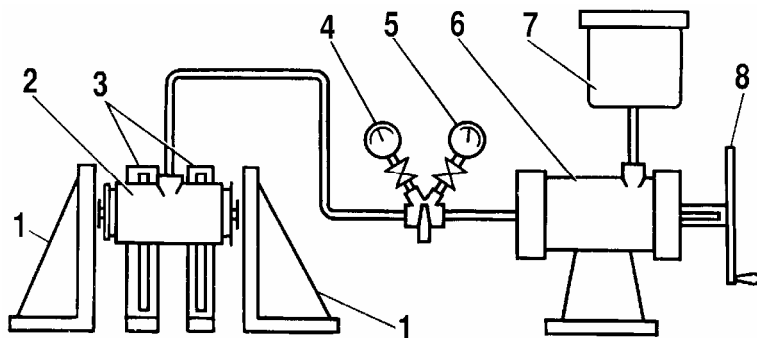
Схема проверки колесных цилиндров задних тормозов:
